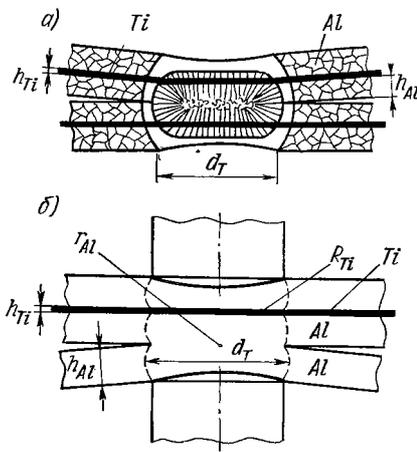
Схема точечно-сварного соединения из биметалла алюминиевого сплава с титаном
